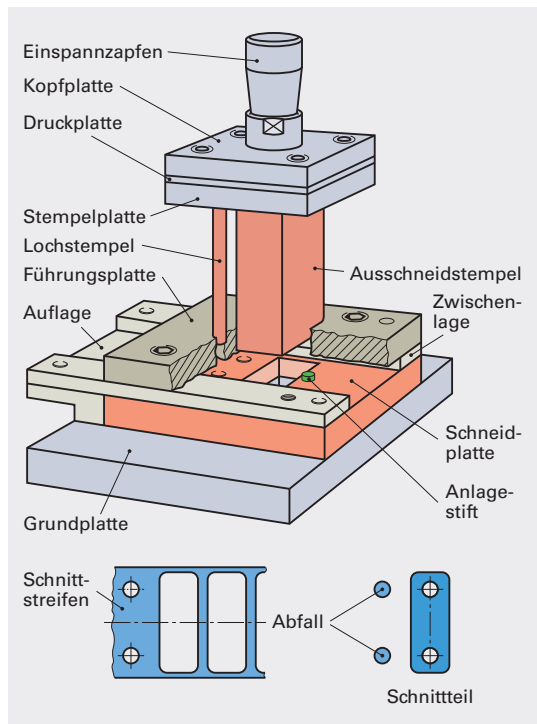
Folgeschneidwerkzeug mit Plattenführung
